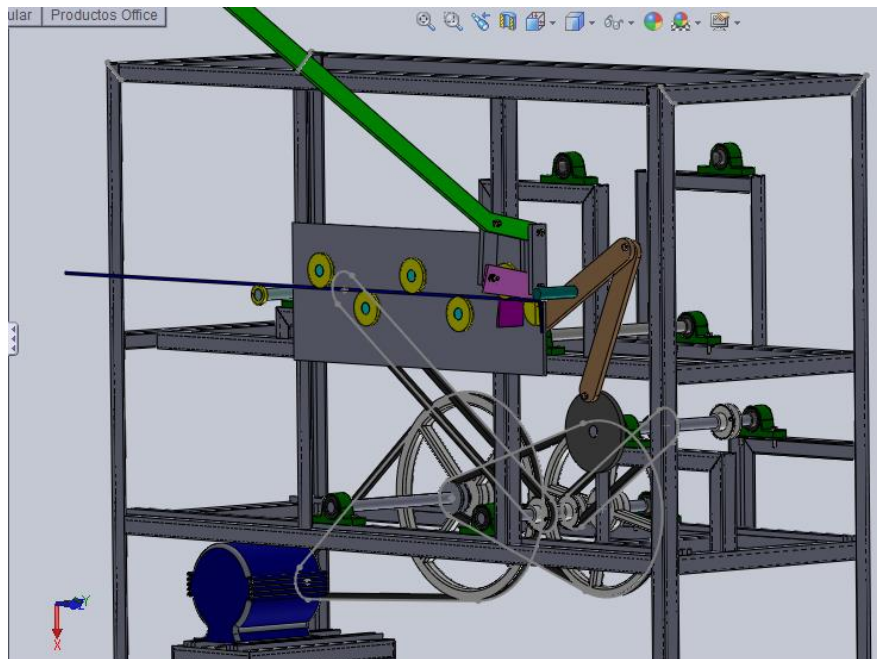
Diseño de la máquina estribadora utilizando SolidWorks
